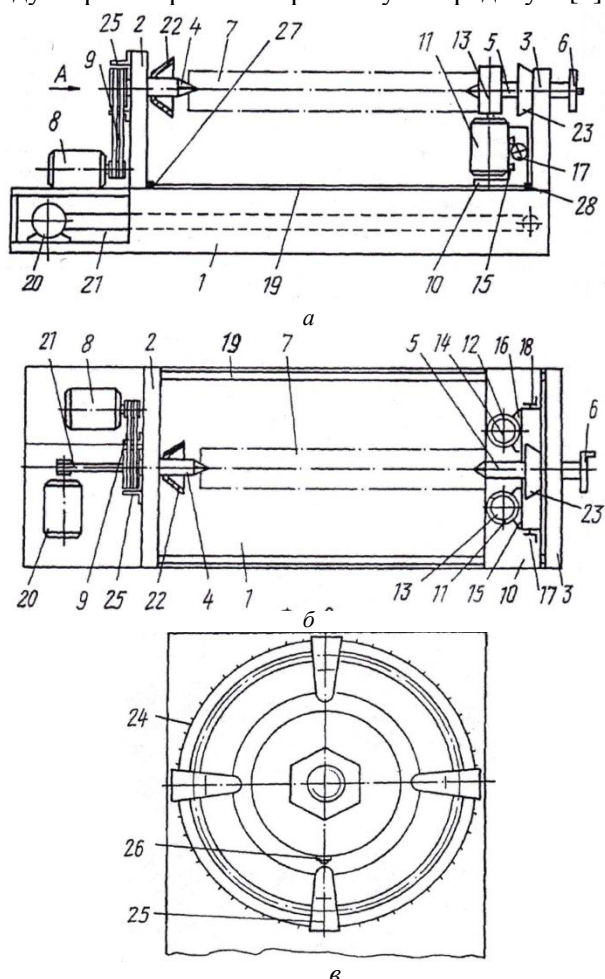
Схема станка для обработки бревен: а – вид спереди; б – вид сверху; в – вид А
